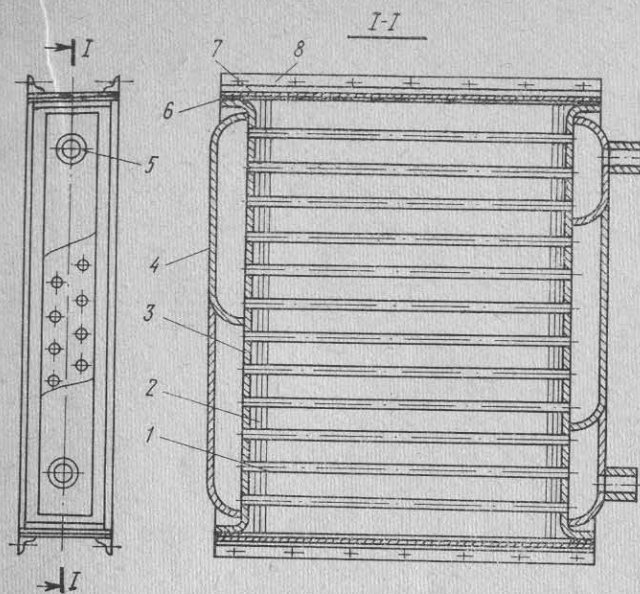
Общий вид многоходового воздушонагревателя с крышками
